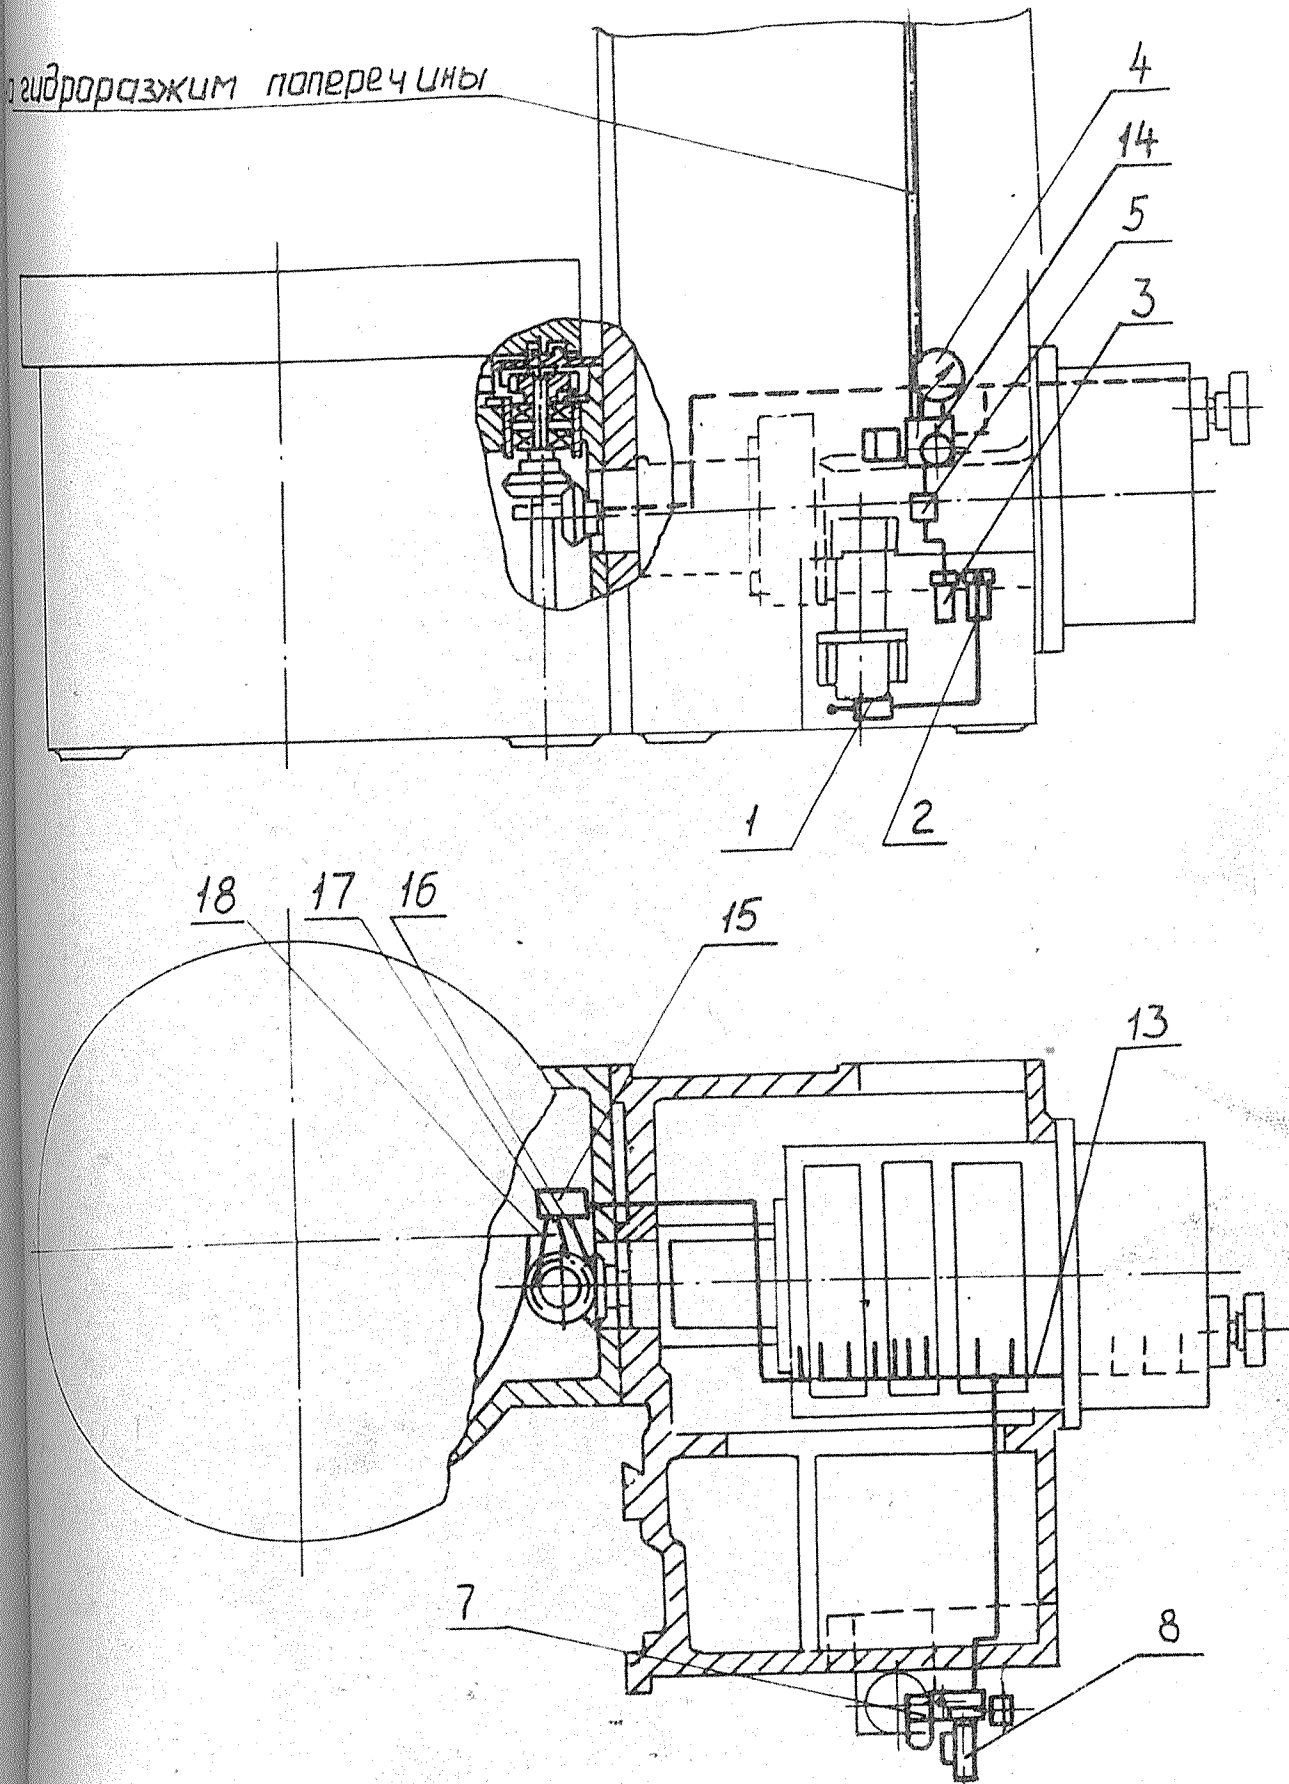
Схема смазки стола и редуктора привода главного движения.
